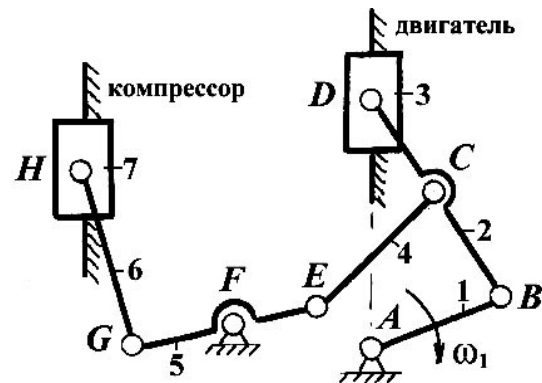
Механизм компрессорного двигателя внутреннего сгорания
